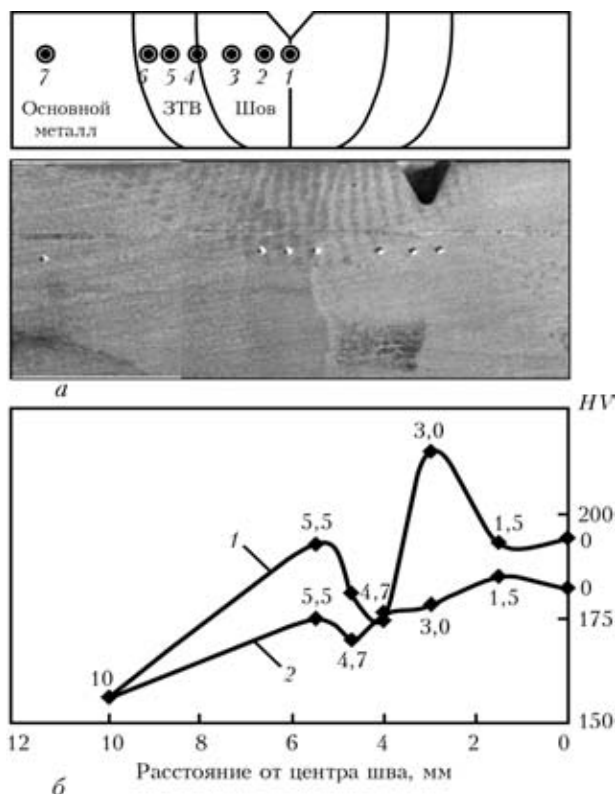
Схема измерения (а) и распределение твердости HV по сечению сварного соединения (б): 1 — первый способ сварки; 2 — второй
